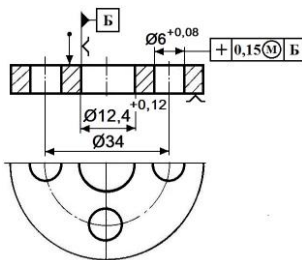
Операционный эскиз обработки заготовки – фланец
